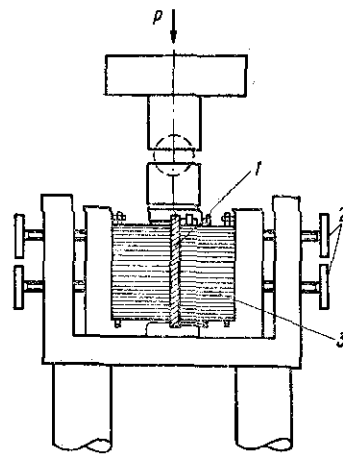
Приспособление для испытания на сжатие тонких пластин из КМ:
